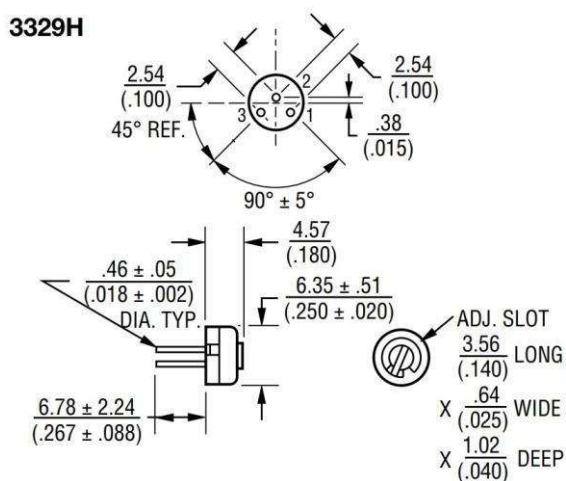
Габаритні розміри резистора підстроювального 3329Н-1
